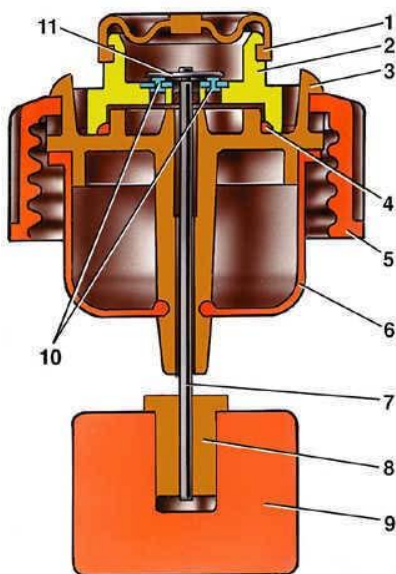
Датчик аварійного рівня гальмівної рідини автомобіля ВАЗ 2110: 1 - захисний ковпачок; 2 - корпус датчика; 3 - основа датчика; 4 - ущільнювальне кільце; 5 - затискне кільце; 6 - відбивач; 7 - штовхач; 8 - втулка; 9 - поплавок; 10 - нерухомі контакти; 11 - рухомий контакт .
